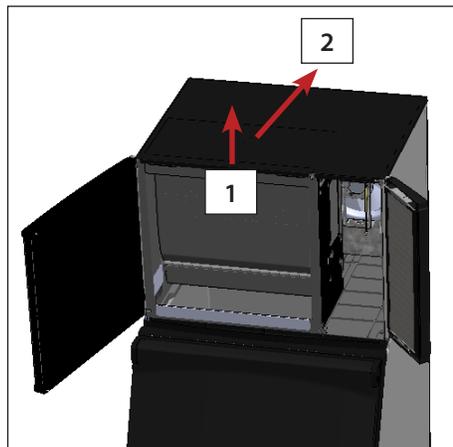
Levez le bord avant, glissez vers l'arrière le panneau supérieur puis soulevez pour le déposer.
